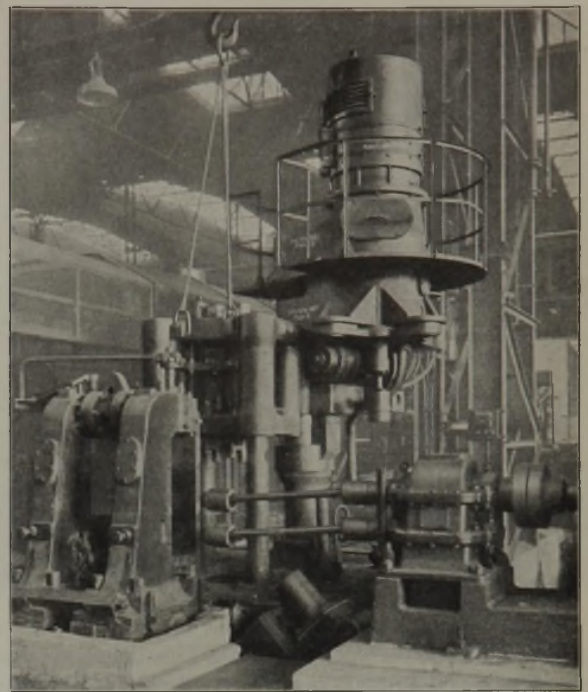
Walzeinbau (Stehwalzengerüst).
